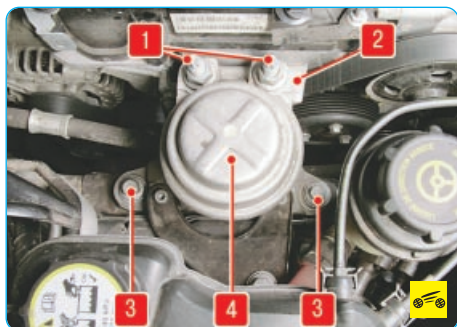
Правая опора подвески силового агрегата: 1 – гайка крепления опоры подвески силового агрегата к кронштейну блока цилиндров двигателя; 2 – кронштейн блока цилиндров двигателя; 3 – болт крепления к лонжерону кузова; 4 – правая опора подвески силового агрегата
